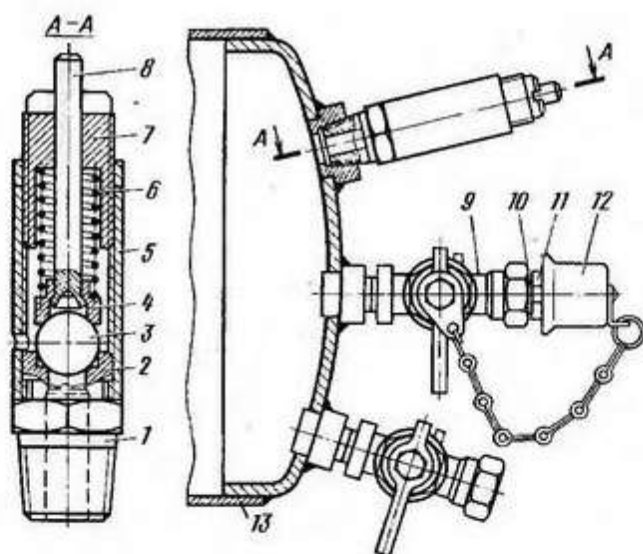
Воздушный ресивер с предохранительным клапаном в сборе:
